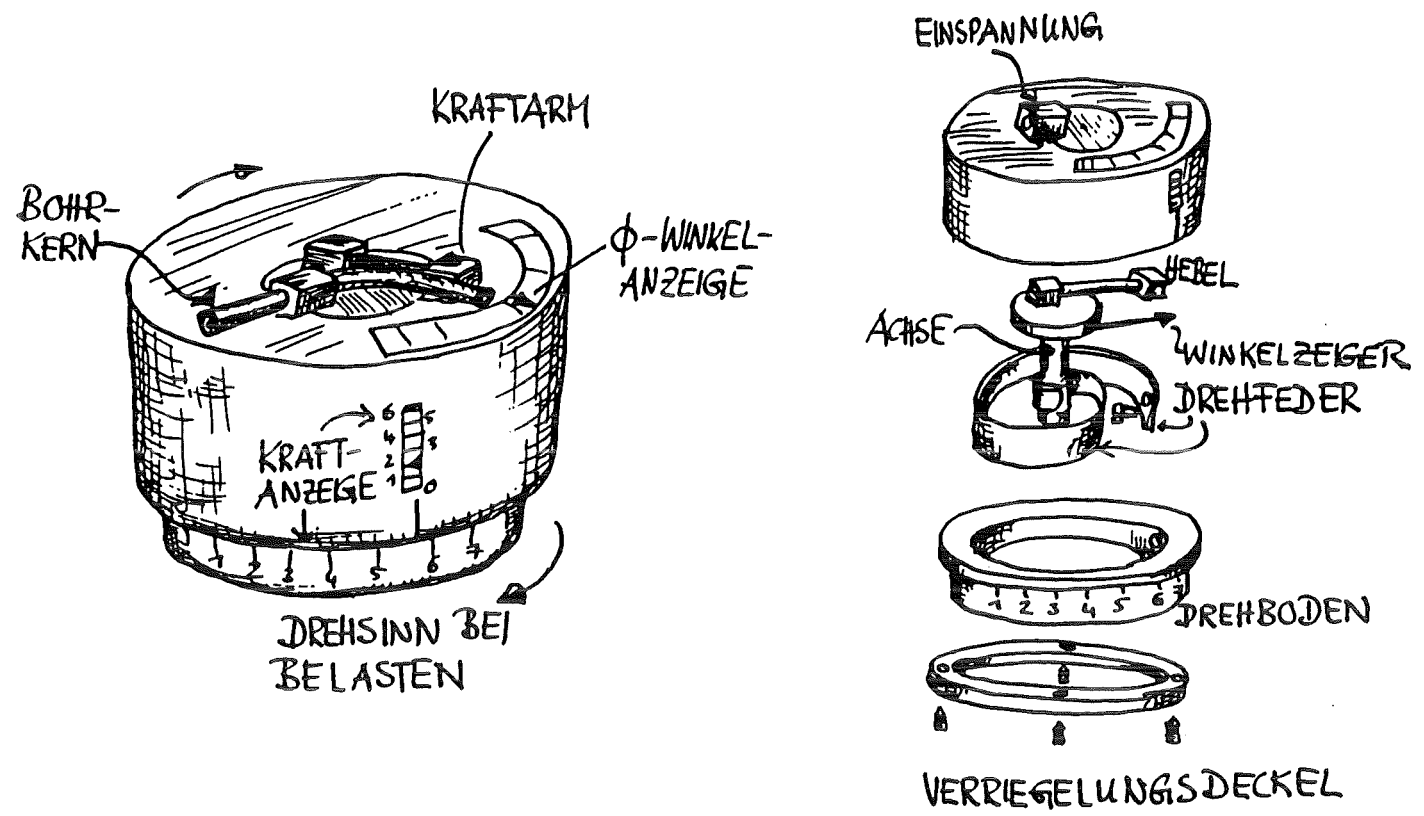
Foto und Explosionsansicht des Fractometer I.
